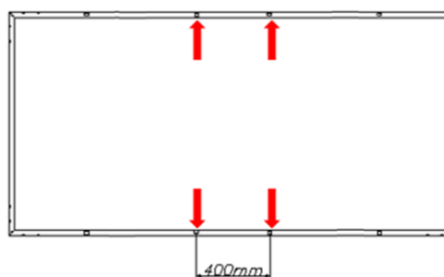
Montaż śrub w czterech zewnętrznych otworach dla 72 ogniw
